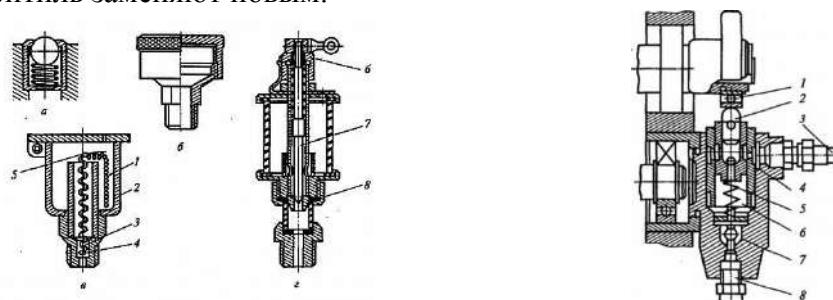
Масленки индивидуального смазывания: а - с шариковым клапаном; б - колпачковая; в - фитильная; г - капельная; 1 - фитиль; 2 - резервуар; 3 - канал; 4 - петля; 5 - усики; 6 - гайка; 7 - игла; 8 - отверстие
